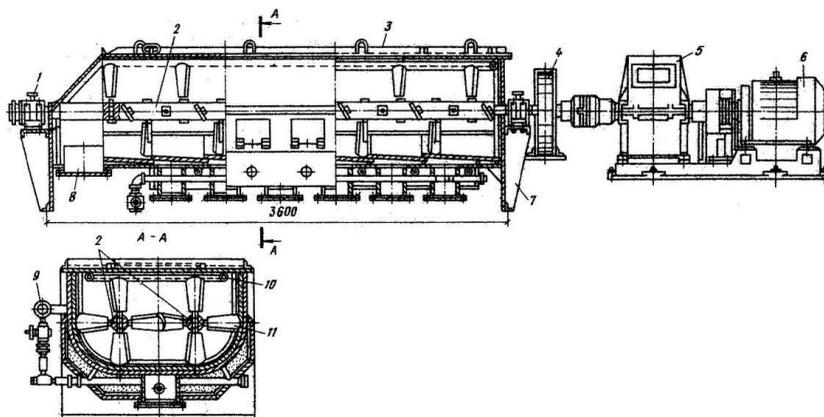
Двухвальный смеситель СМ-246: 1 – подшипники; 2 – перемешивающие валы; 3 – корпус смесителя; 4 – шестеренчатая передача; 5 – редуктор; 6 – электродвигатель; 7 – опорные стойки; 8 – выгрузочное отверстие; 9 – трубопровод для подачи пара; 10 – трубопровод для подачи воды; 11 – смесительные лопасти
